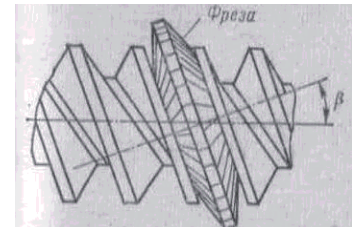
Нарезание винтовой поверхности червяка фрезерованием
